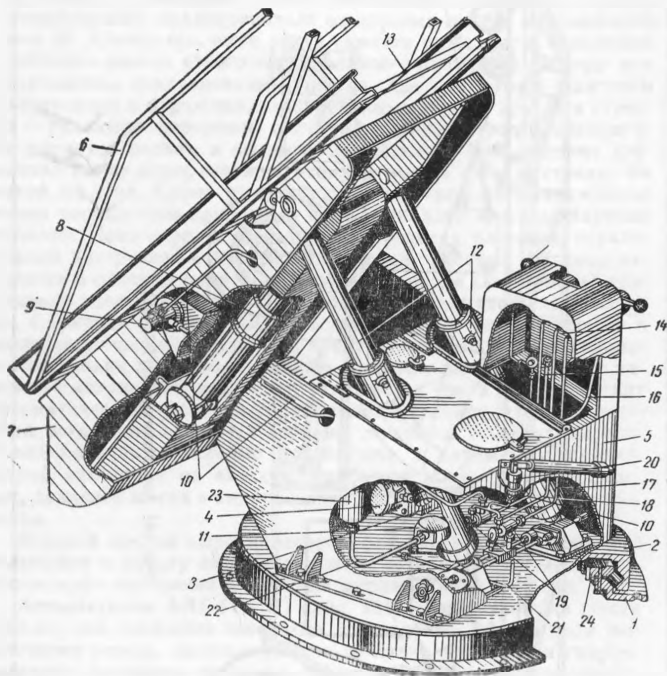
Подъемно-поворотное основание и механизм гидропроводов
